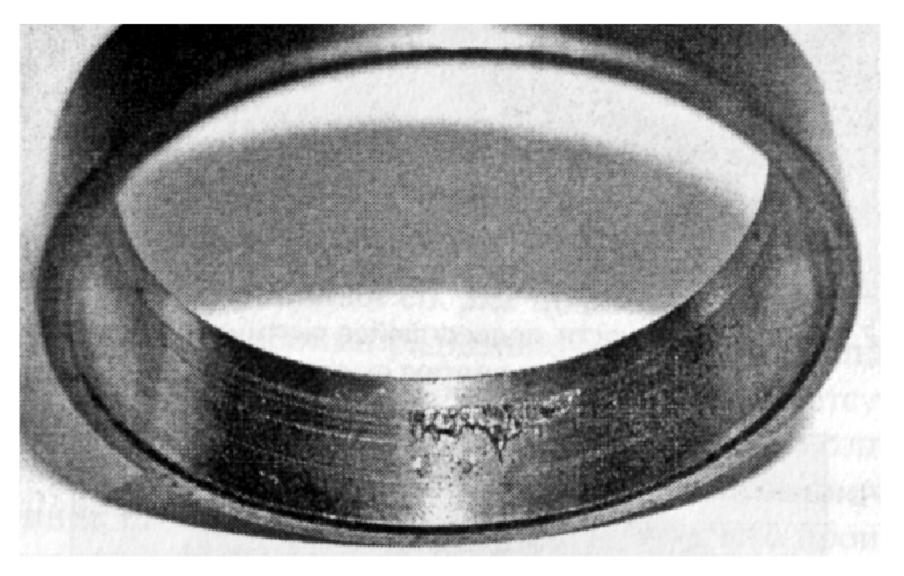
Обойма подшипника с очагом усталостного изнашивания
